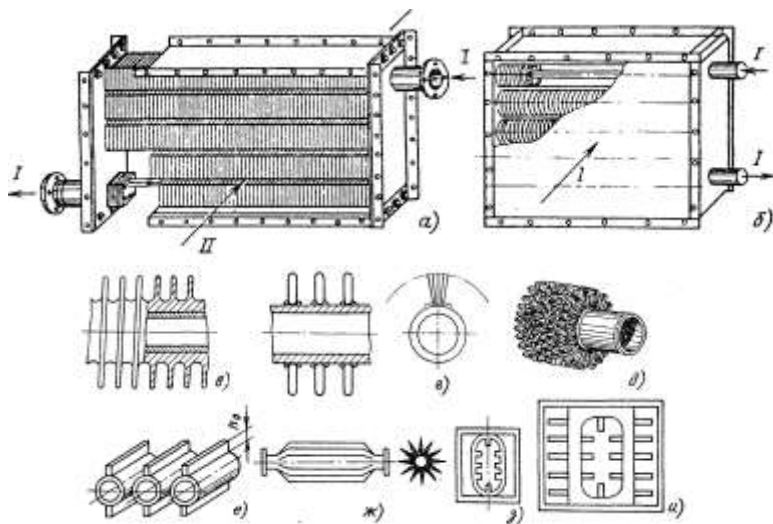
Ребристые теплообменники для нагрева воздуха и элементы их поверхностей нагрева:
